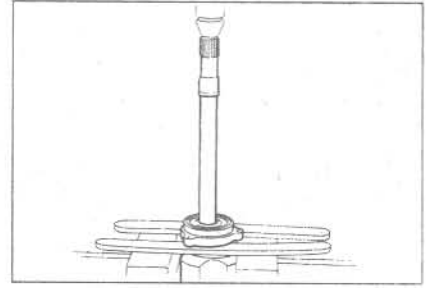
Установка подшипника держателя на вал внутреннего ШРУСа (Глава 4)
